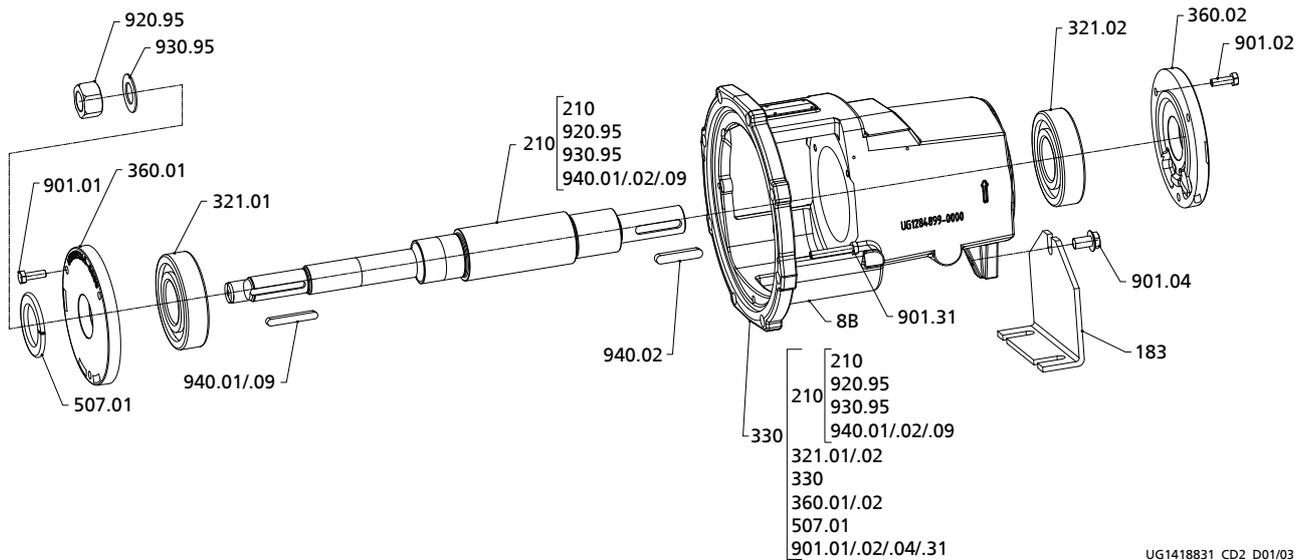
Исполнение с усиленной подшипниковой опорой (узел вала 50 и 60)
